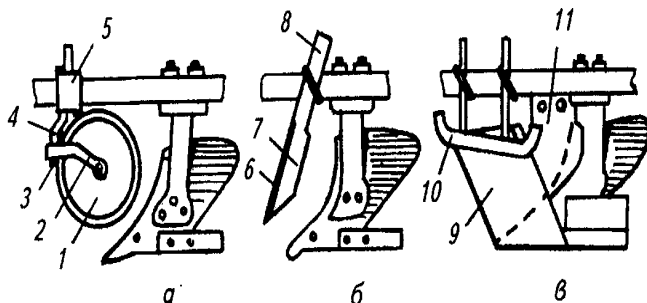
Ножи плуга: а – корпус плуга с дисковым ножом; б – корпус плуга с черенковым ножом; в – корпус болотного плуга с плоским ножом и опорной лыжей: 1 – диск; 2 – вилка; 3 – корончатая гайка
